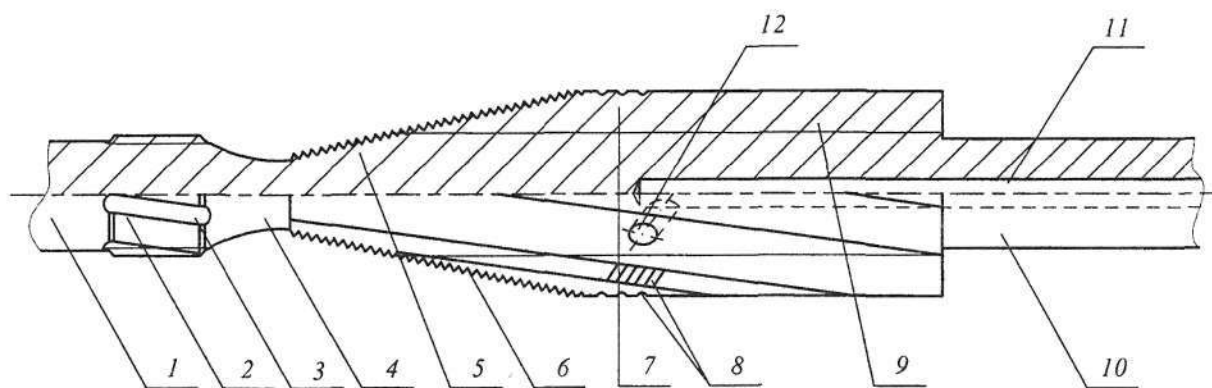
Вариант инструмента для обработки внутренних винтовых поверхностей
